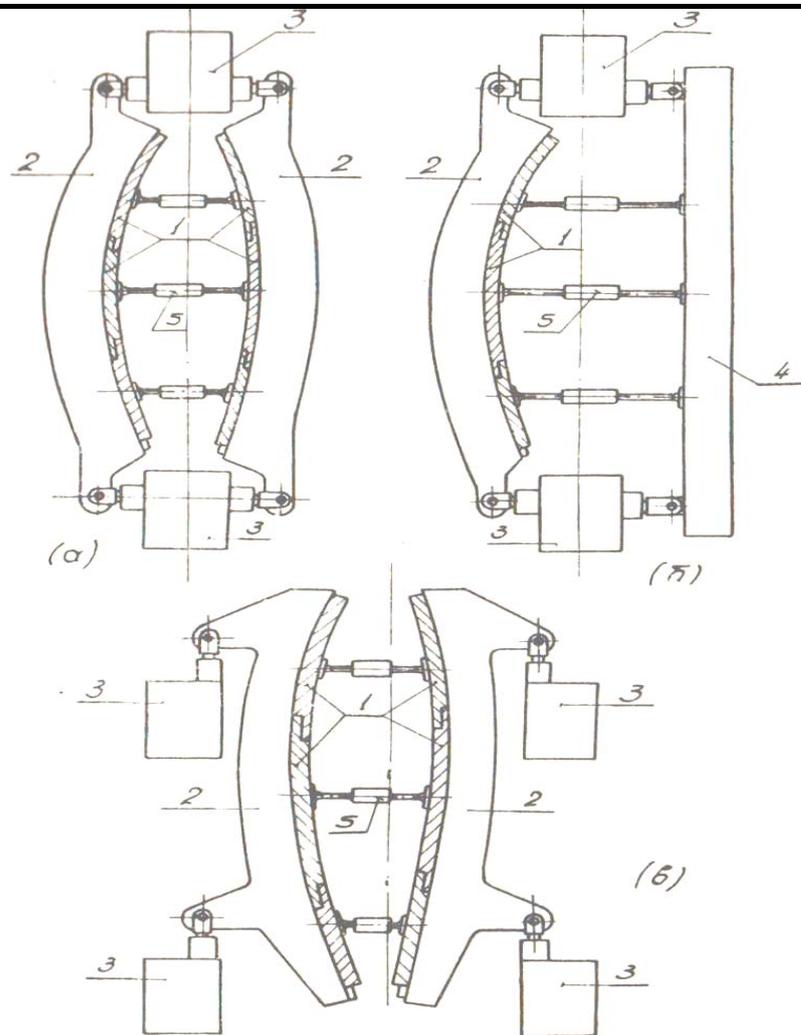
1—панели; 2 — рубильники; 3 — балки стапеля; 4 — опорная балка; 5 — распорный механизм.
